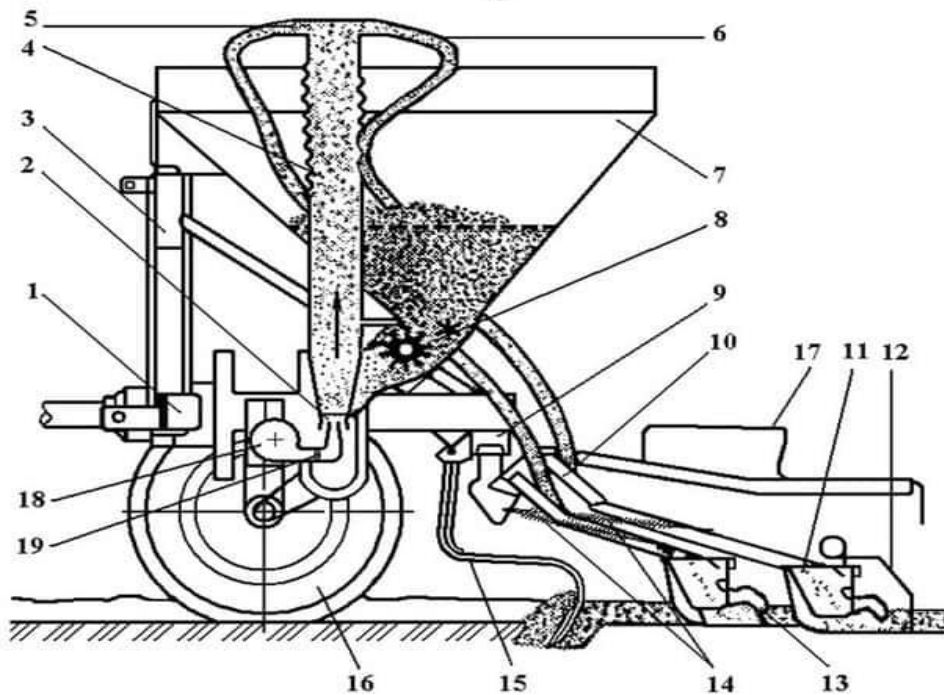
Схема работы трехсеялочного агрегата:
